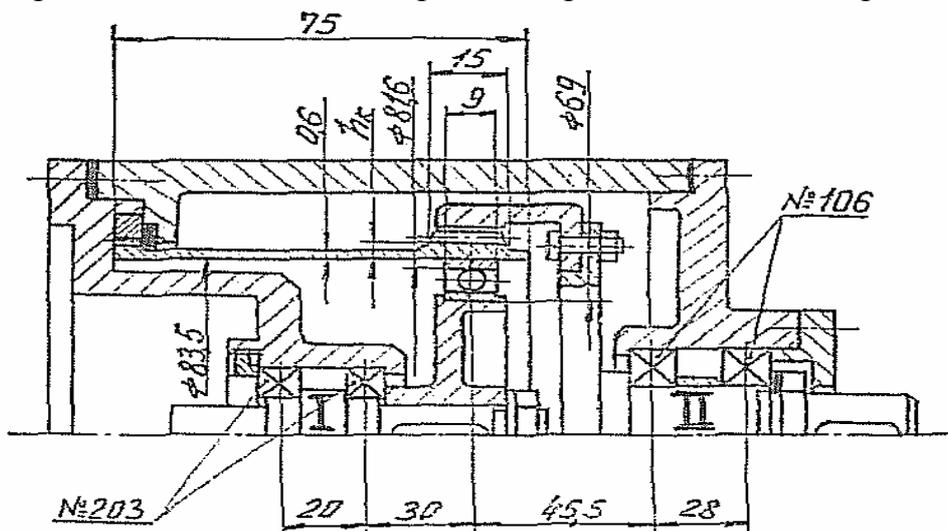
Конструктивная схема волнового зубчатого редуктора
